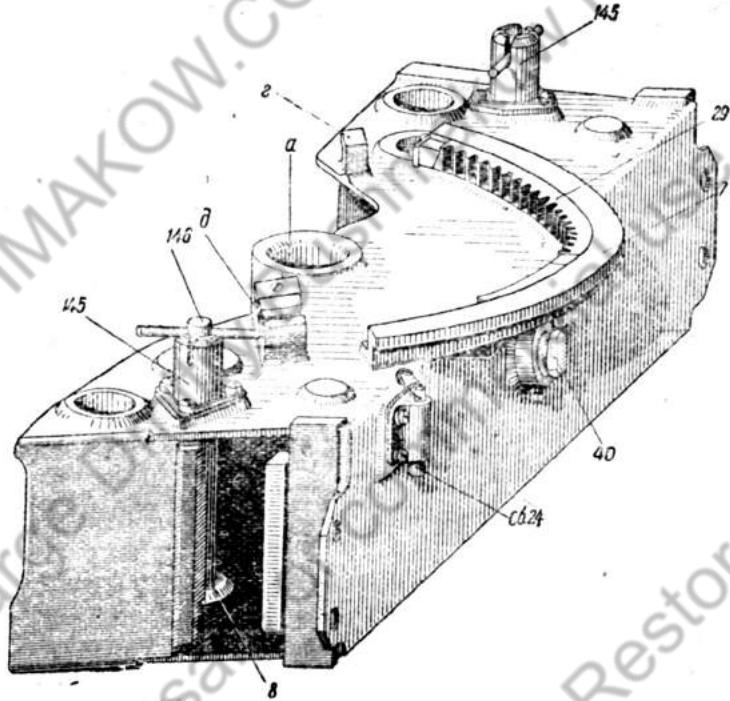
Корпус нижнего станка (сб. 06). Вид спереди и справа:
